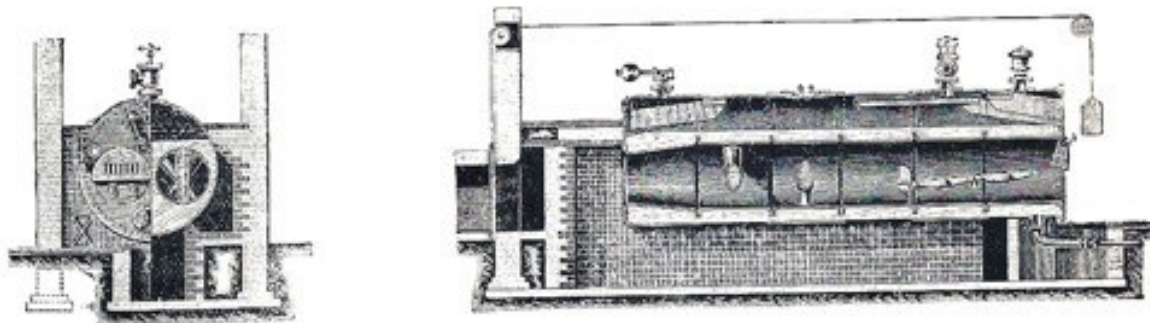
Zvětšené výřezy z výkresu na Obr. 5.2.2.24 s označením jednotlivých částí parního systému a naznačením toku spalin ve spalinových cestách [zdroj: [71], upraveno: autor]
